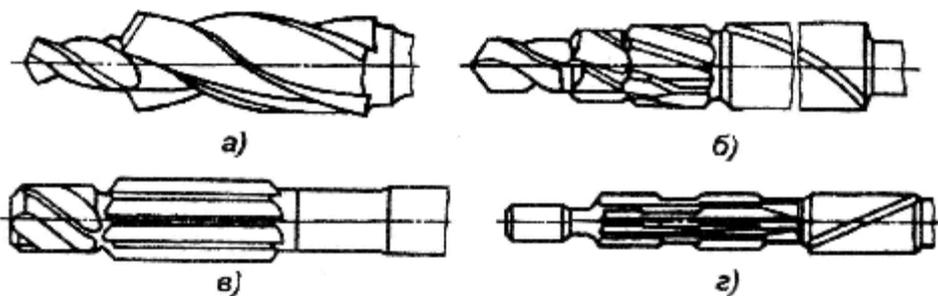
Комбинированные инструменты: а – сверло – зенкер; б – сверло – зенкер – развертка; в – зенкер – развертка; г – развертка – развертка
